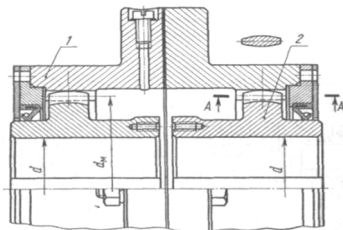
Зубчаста муфта: 1-обойма; 2-втулка
